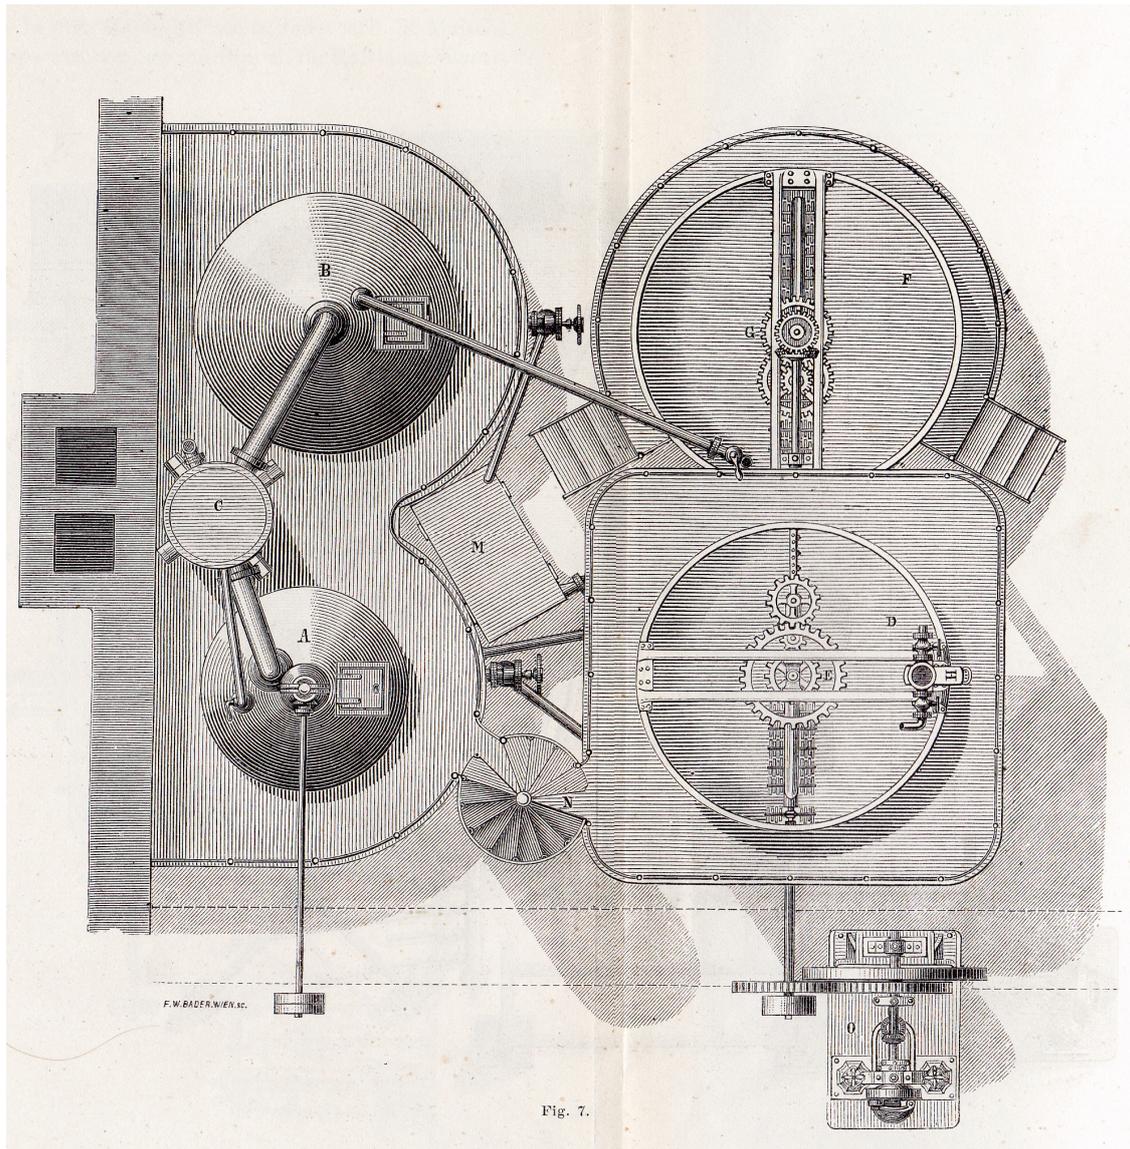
Grundriss des kompletten Brauapparats der Firma V. Prick im Jahr 1873
